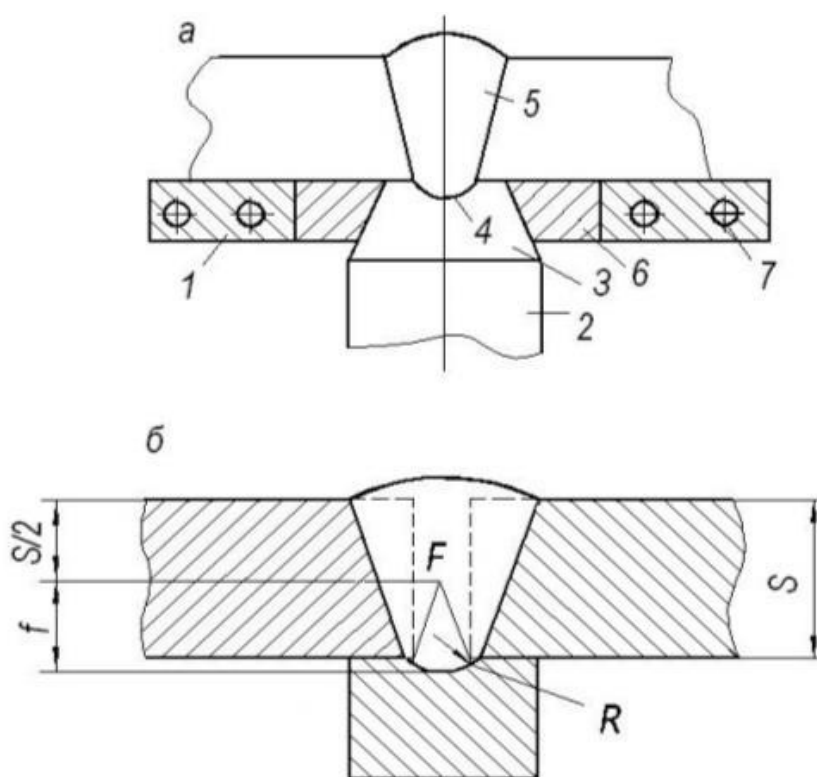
Устройство для формирования: а - обратная сторона сварного шва; б - формирующая канавка: R - радиус формирующей канавки; S - толщина свариваемых деталей; F - фокусное расстояние
